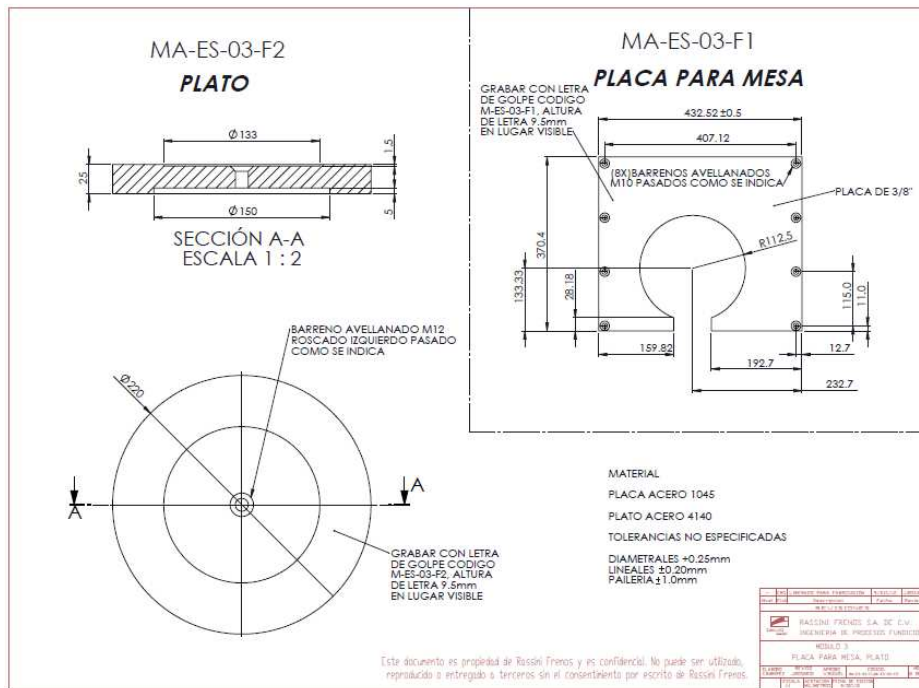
Plano de fabricación plato giratorio y placa para mesa
